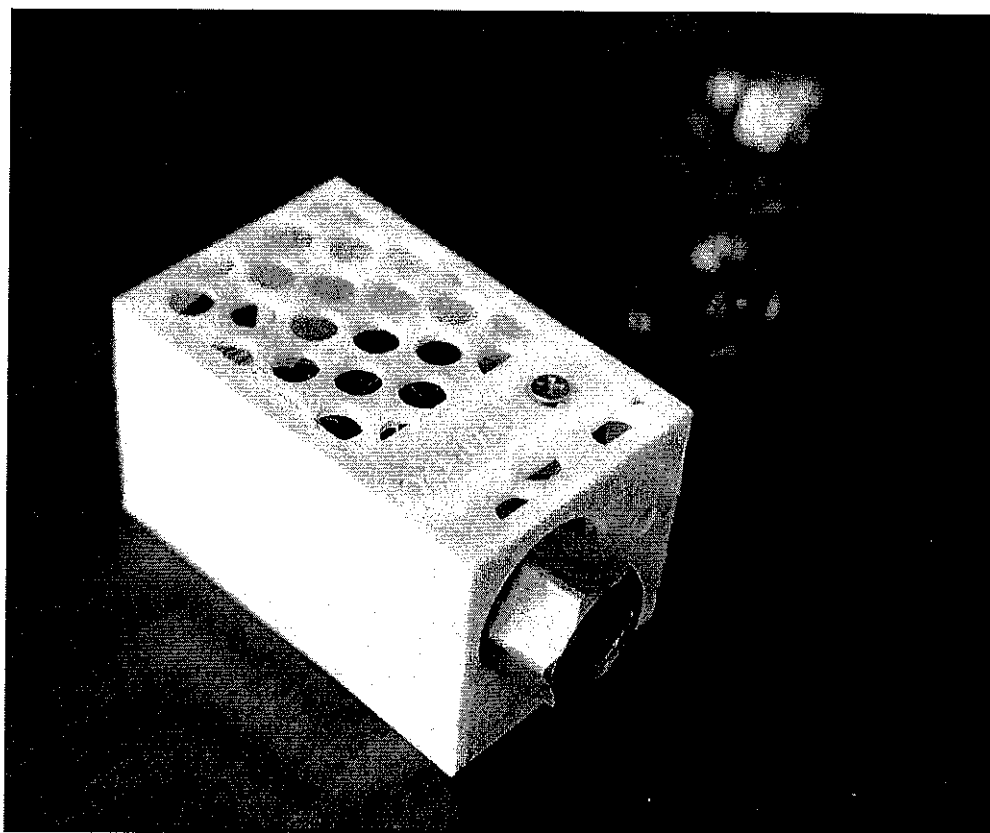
Ensemble carcaza, chasis y sensor de flujo.
